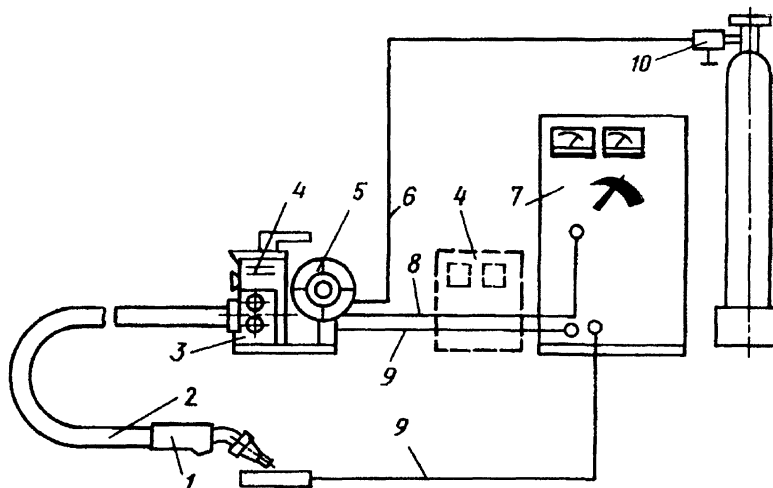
Схема шлангового полуавтомата для сварки в среде защитного газа
